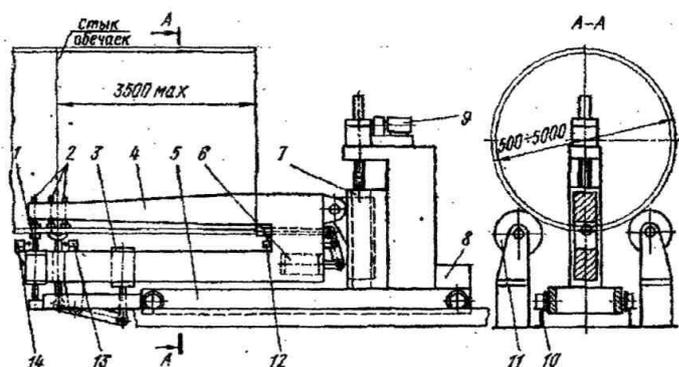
Установка для сборки обечайек по кольцевым стыкам
